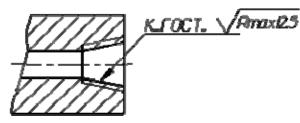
Пример обозначения шероховатости внутренней конической резьбы
